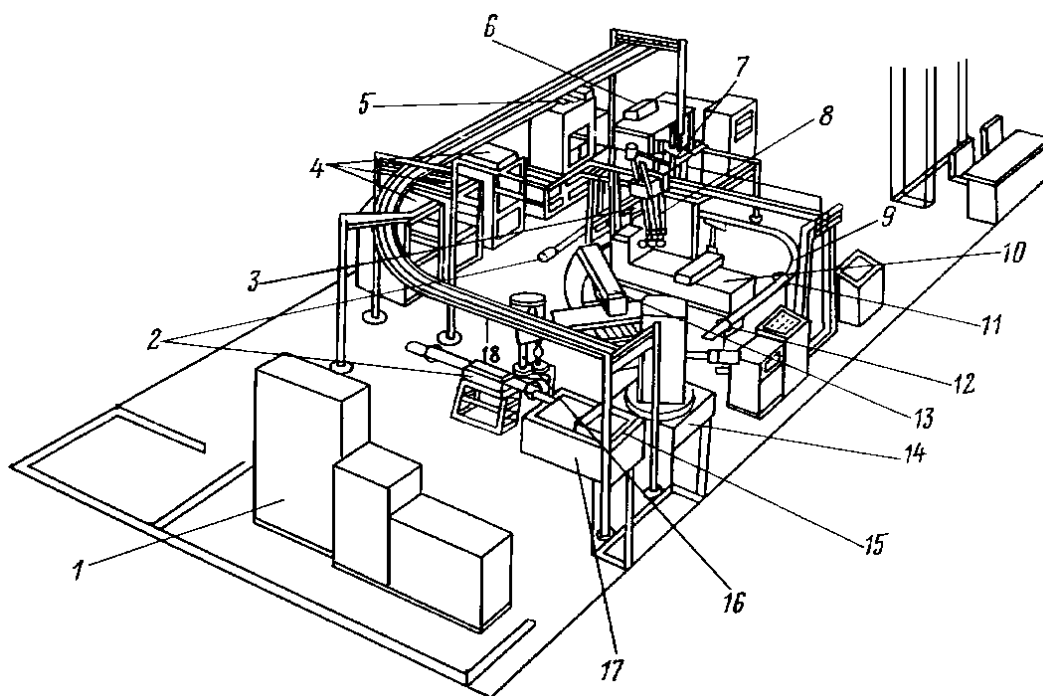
Автоматична лінія фірми Hitachi з механічними руками і роботами для оброблення вала ротора малогабаритного електродвигуна: 1 – ЕОМ керування лінією; 2 – механічна рука для переміщення заготовок уздовж однієї осі в накопичувачах (на майданчиках) № 1 і 2; 3 – накопичувач (майданчик) № 1 для перезавантаження заготовок; 4 – стелажі № 1, 2 і 3 для піддонів з заготовками і валами різних типорозмірів; 5 – підвісний робот для передачі важких піддонів з заготовками; 6 – пульт уведення програм оброблення деталей; 7 – робот для передачі заготовок валів; 8 – портальний робот (здвоєна механічна рука) для завантаження токарного верстата; 9 – лоток; 10 – токарний патронний автомат; 11 – визначник заготовок, що підлягають обробленню на токарному верстаті 10; 12 – перемикаючий пристрій для передачі заготовок роботу 14; 13 – горизонтально-фрезерний верстат-автомат; 14 – підлоговий стаціонарний робот для завантаження фрезерного і свердлильного верстатів; 15 – піддон для готових виробів; 16 – вертикально-свердлильний верстат-автомат; 17 – накопичувач (майданчик) для перезавантаження заготовок; 18 – напрямна для руху робота 5
